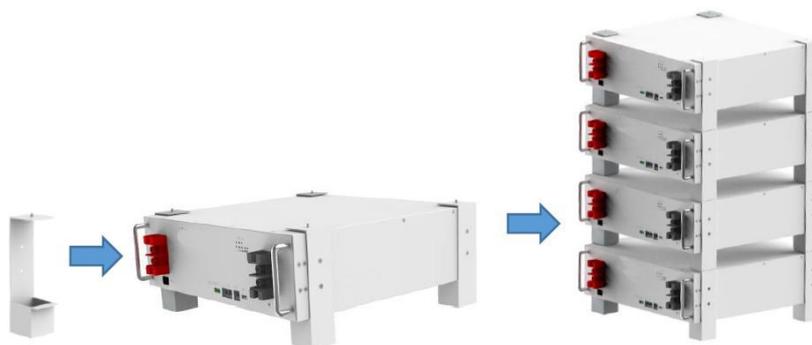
Instalación del módulo de batería (Un posible procedimiento de instalación de la batería)
